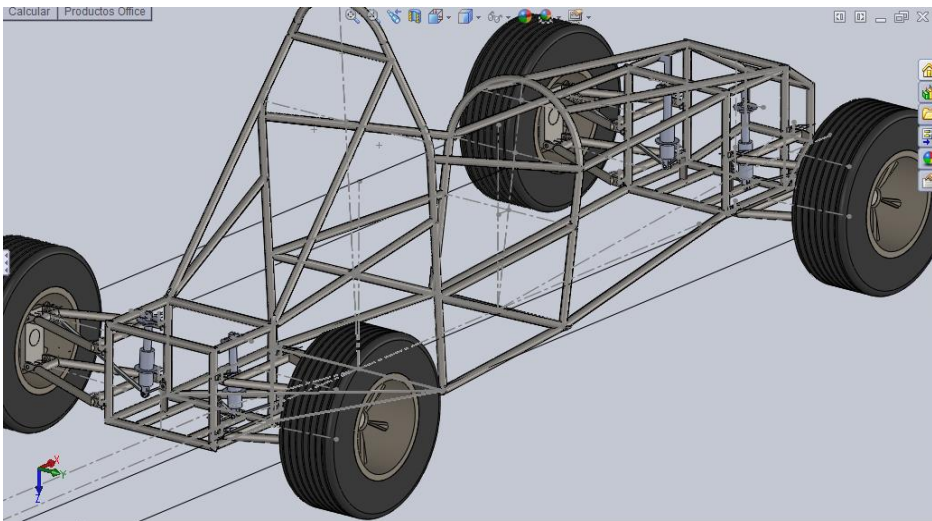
Vista isométrica del ensamblaje Pull-rod
